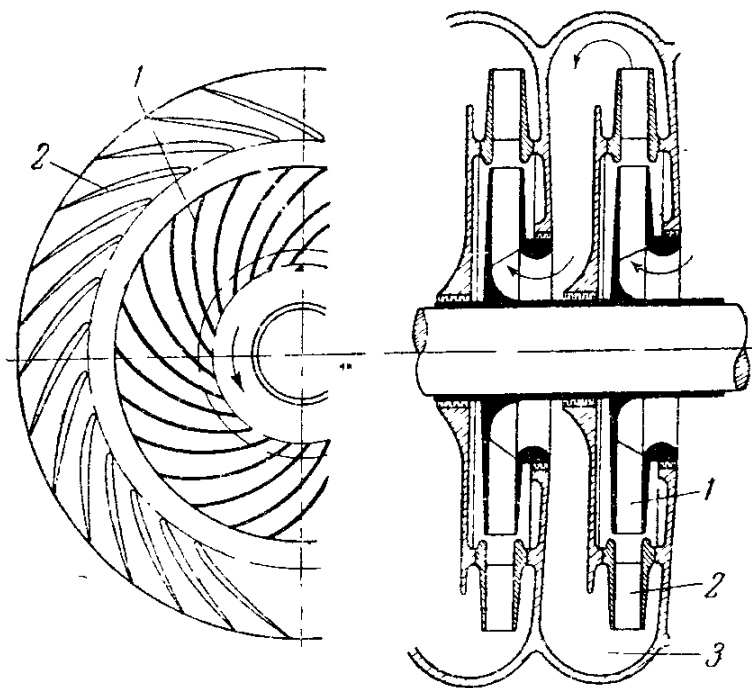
Разрез рабочего колеса турбокомпрессора.
